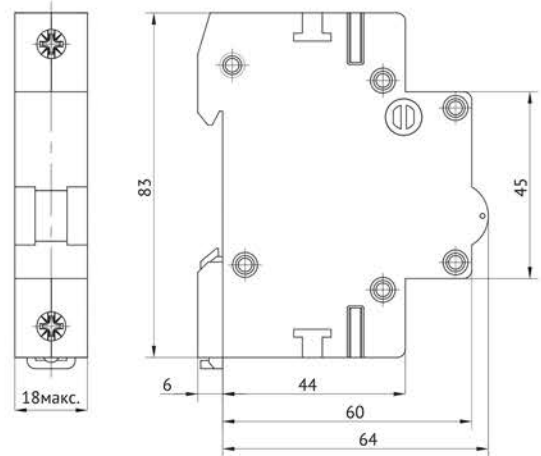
Габаритные, установочные и присоединительные размеры сигнальной лампы типа OptiDin SL63
